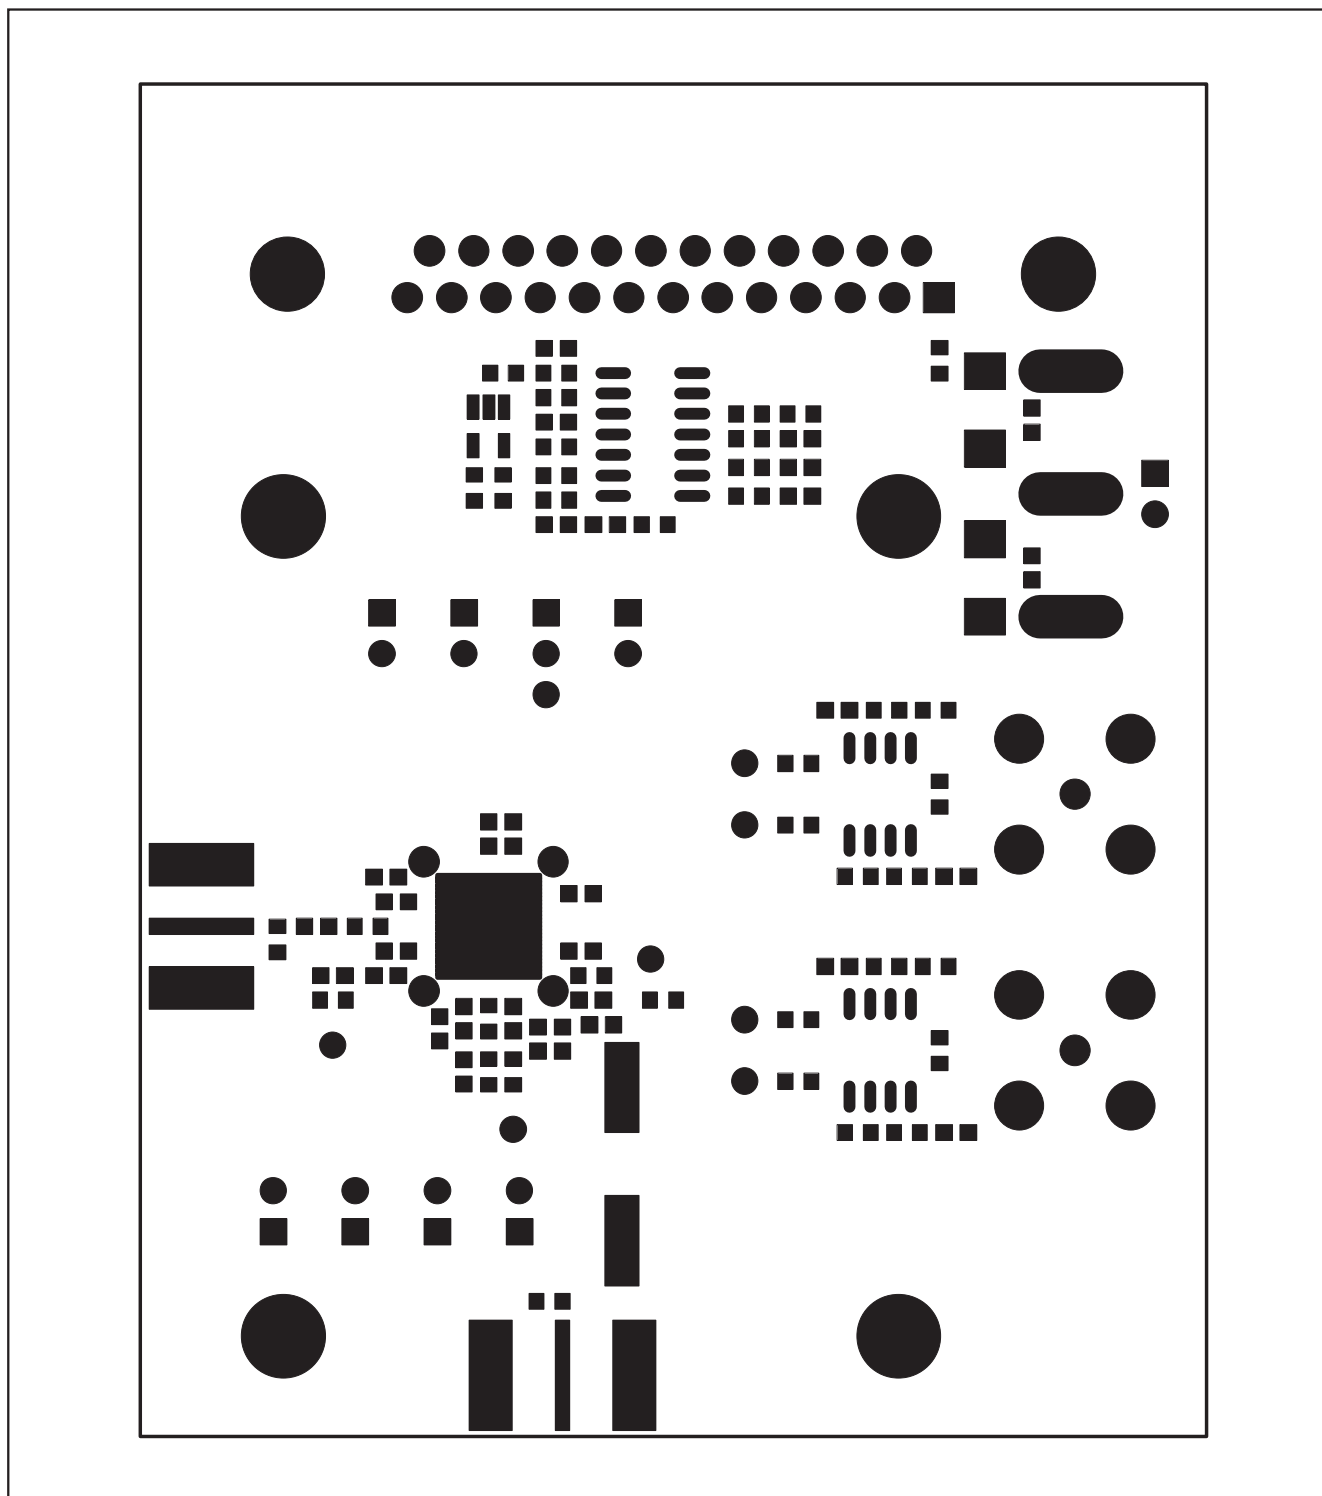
MAX2112评估板PCB布局—顶层阻焊层
